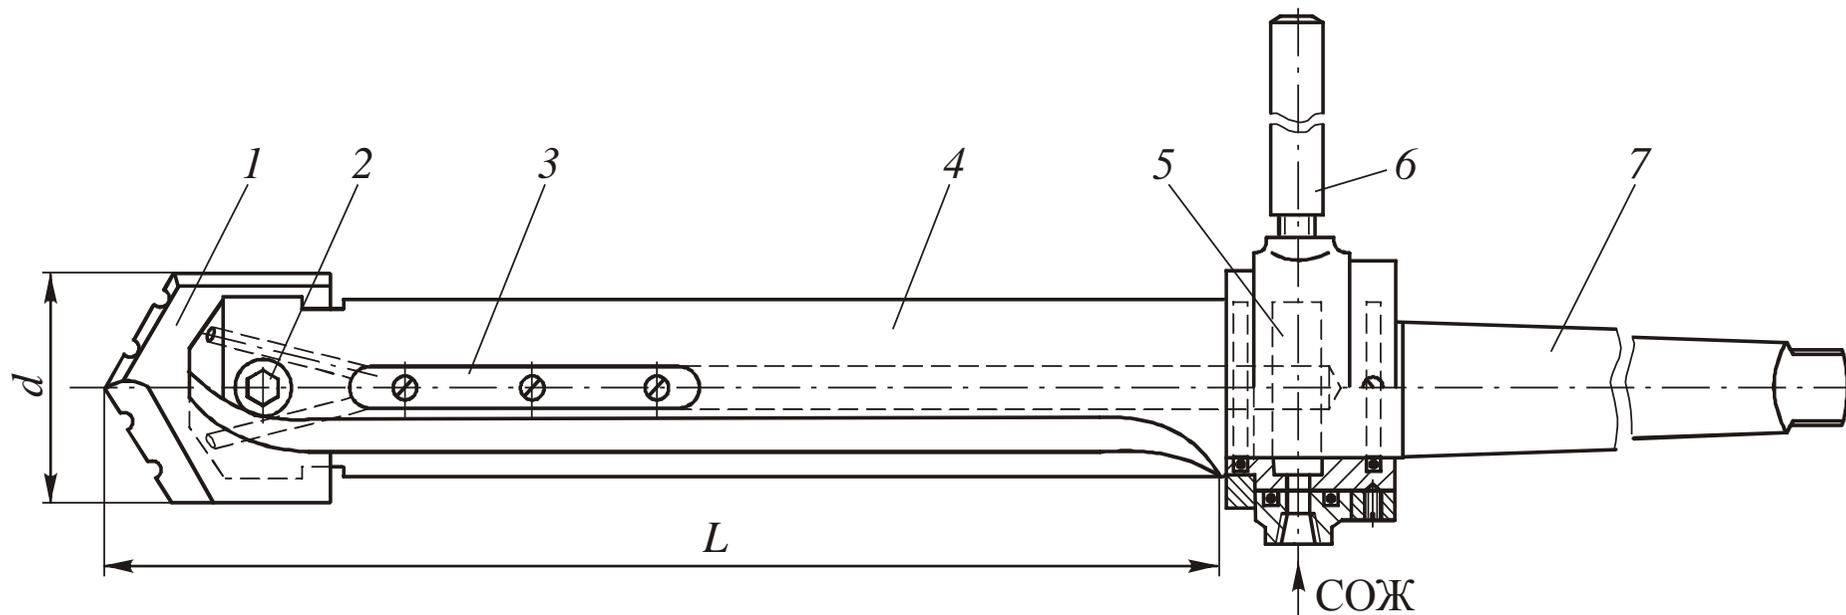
Сборное перовое сверло для сверления глубоких отверстий:
